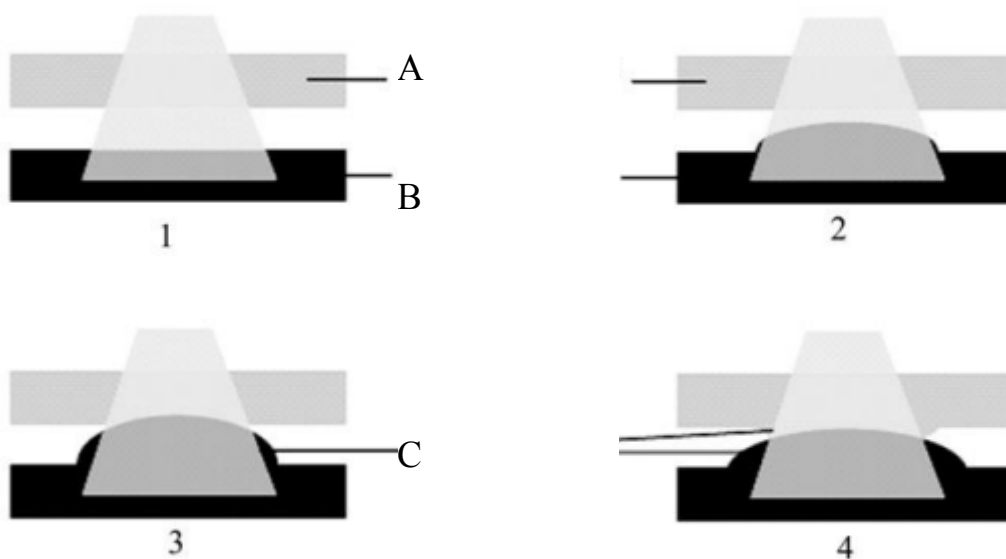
Схема лазерного зварювання матеріалів з полімеру: А – плівка прозора; В – плівка абсорбуюча; С – розплав.
